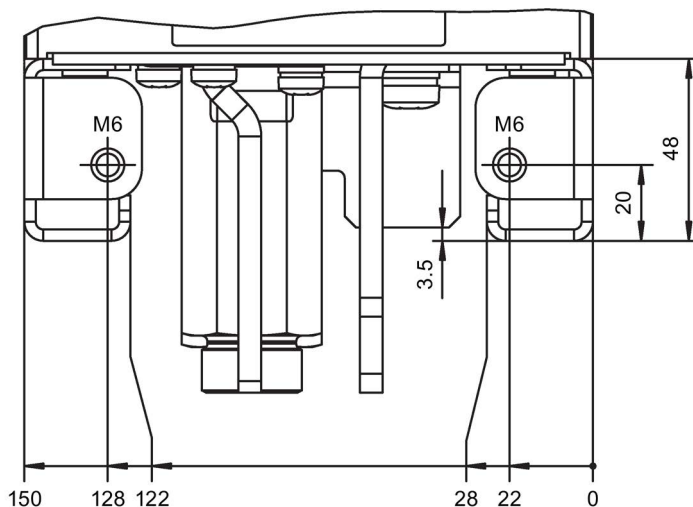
Профиль шины модуля двигателя, типоразмер FXL (размеры указаны в мм)
